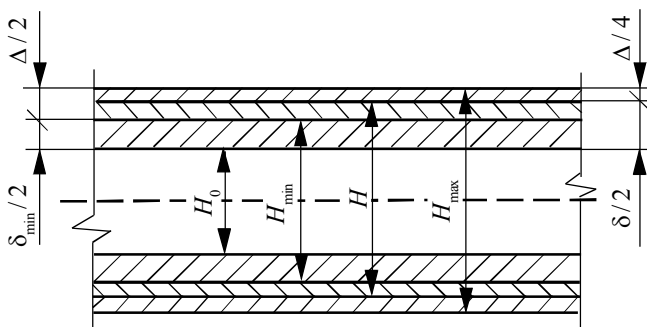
Припуски и допуски на ковку по ГОСТу 7062—90
